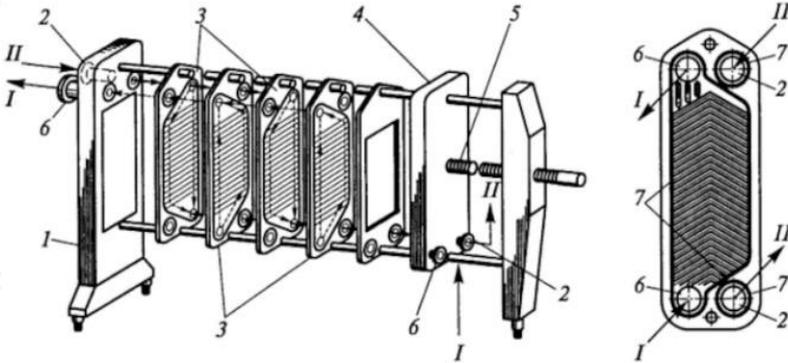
Разборный пластинчатый теплообменник на двухопорной раме:
